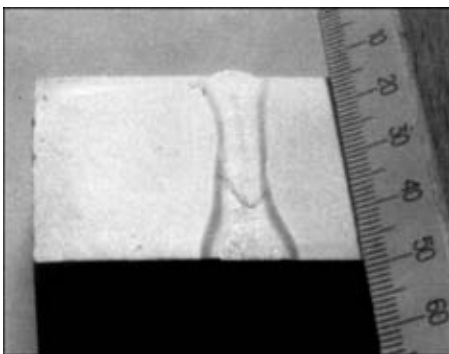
Макрошлиф двухстороннего шва при сварке пакета из двух лопаток со стороны их хвостовой части
